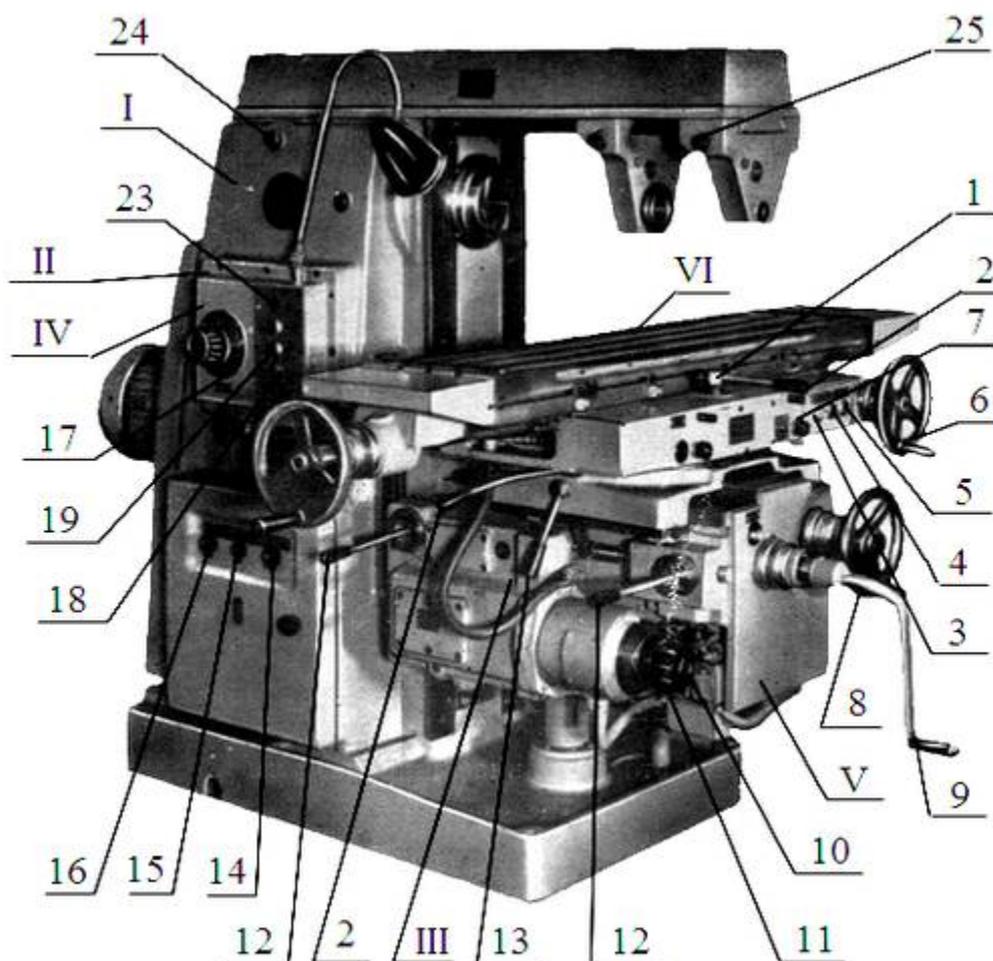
Общий вид консольно-фрезерного станка 6М82
